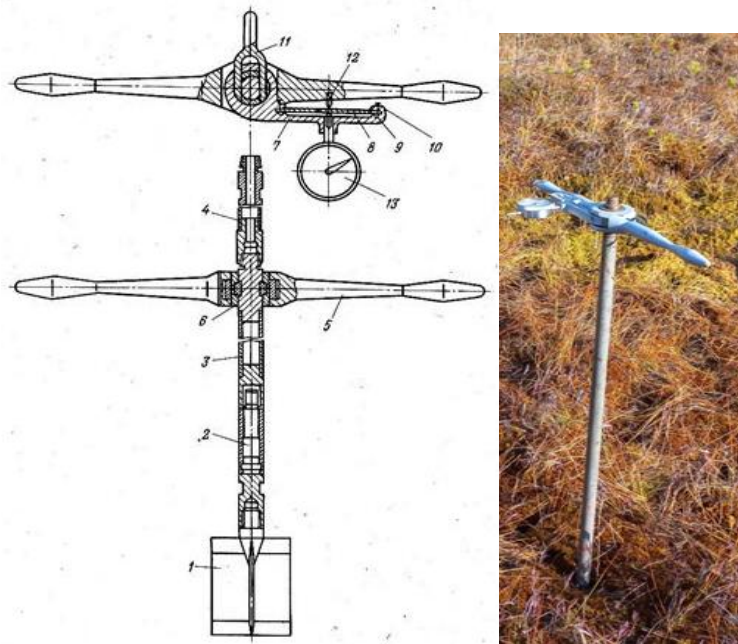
Сдвигомер-крыльчатка СК-10: 1 – крыльчатка; 2 – корпус; 3 – штанга; 4 – втулка крепления; 5 – рукоятка; 6 – втулка; 7 – корпус динамометра; 8 – плоская пружина; 9 – призма; 10 – крепление пружины; 11 – вилка для фиксации корпуса динамометра на штанге; 12 – нажимное устройство; 13 – индикатор часового типа.
